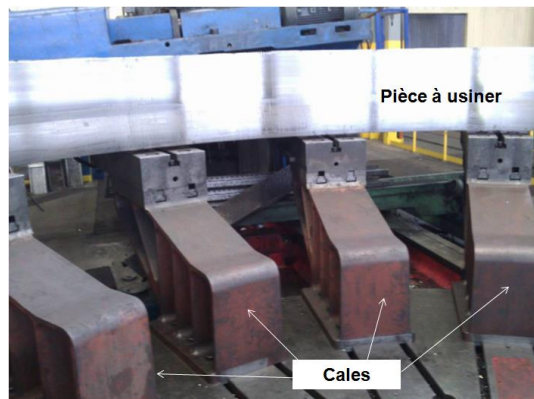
Exemple du montage d'une couronne sur le plateau de la machine-outil.
